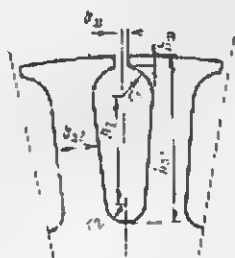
Форма и размеры полузакрытого овального паза якоря.
